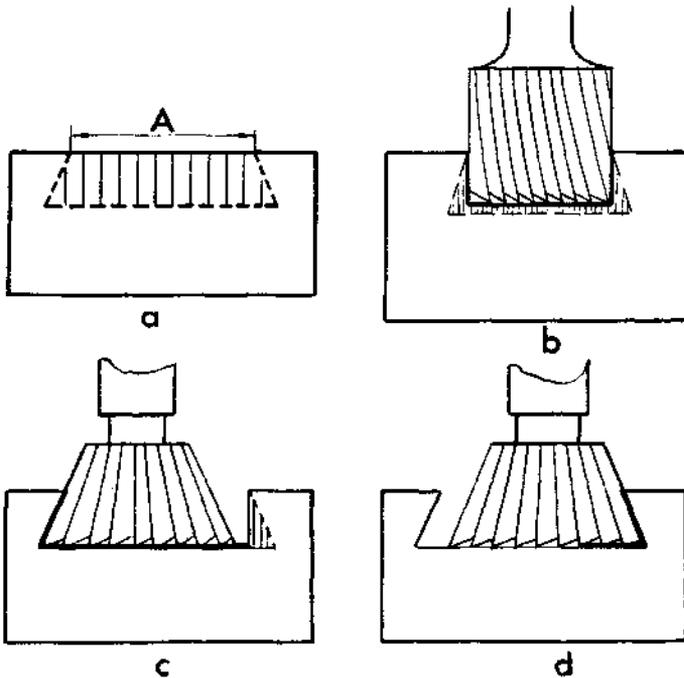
Proceso de mecanizado con fresa de una cola de milano en una pieza cuadrada: a, perfil a obtener; A, medida en anchura; b, desbaste con una fresa cilíndrica. El diámetro debe ser $< A$; c, fresado de un flanco en ángulo; d, fresado del segundo flanco.
